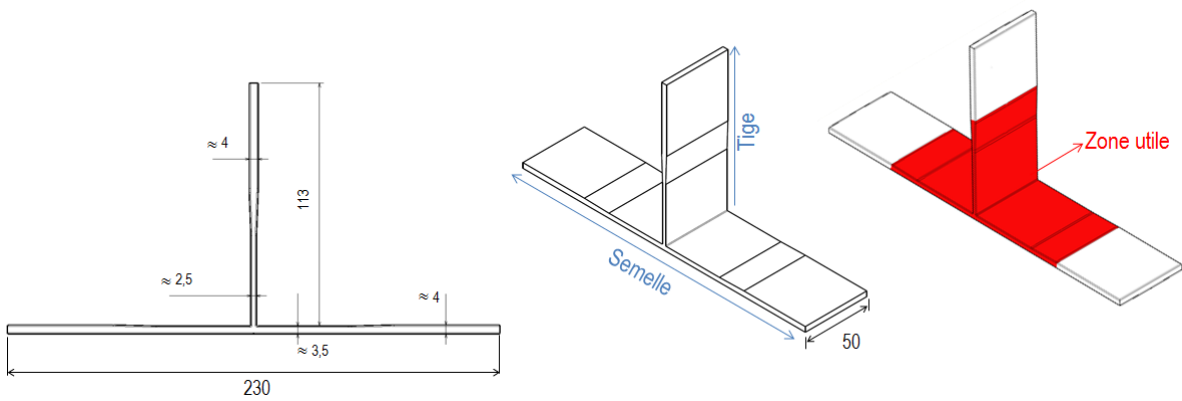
Géométrie et zone utile des éprouvettes T-Bone, dimensions en [mm].
